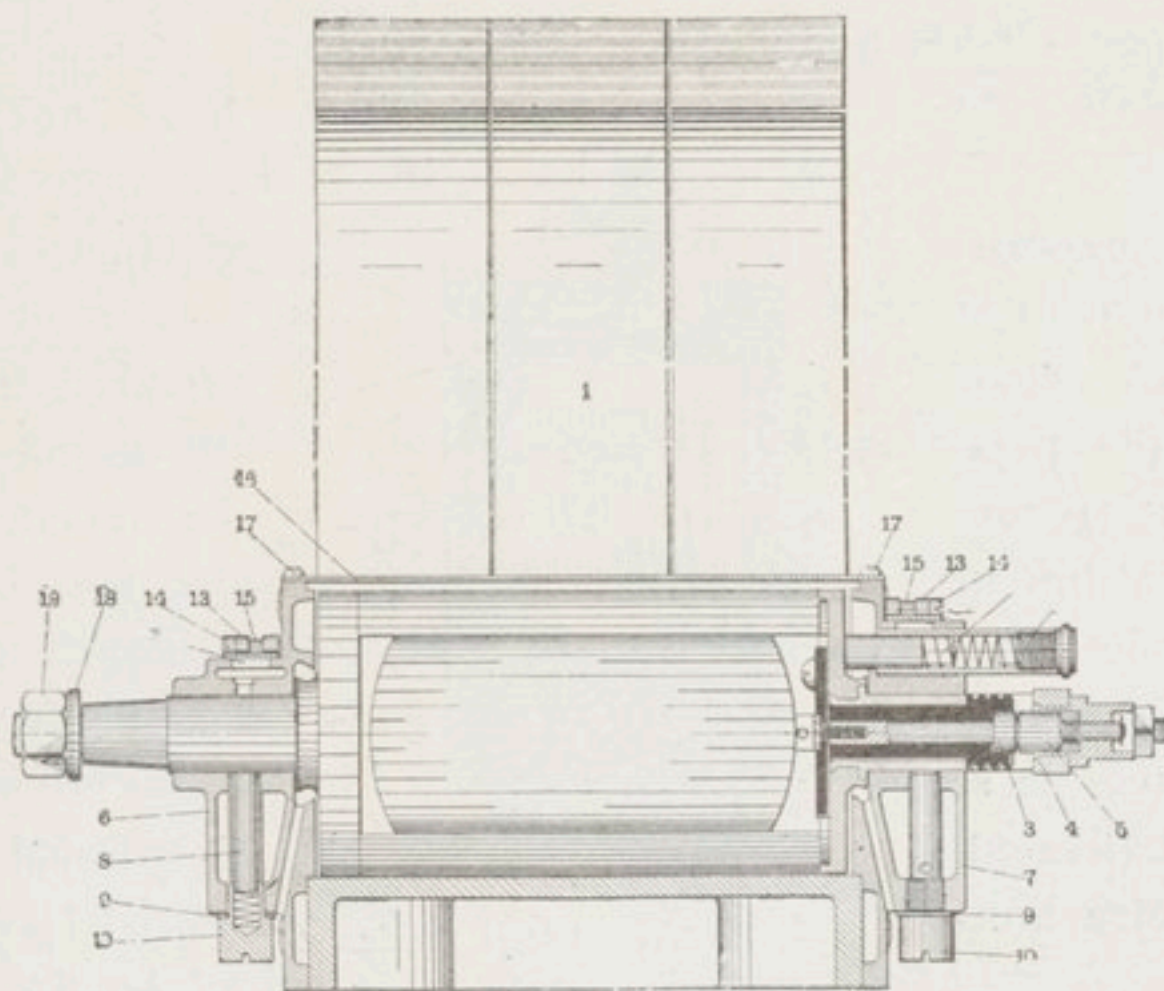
Magnéto Bosch à rupture. Coupe verticale.
